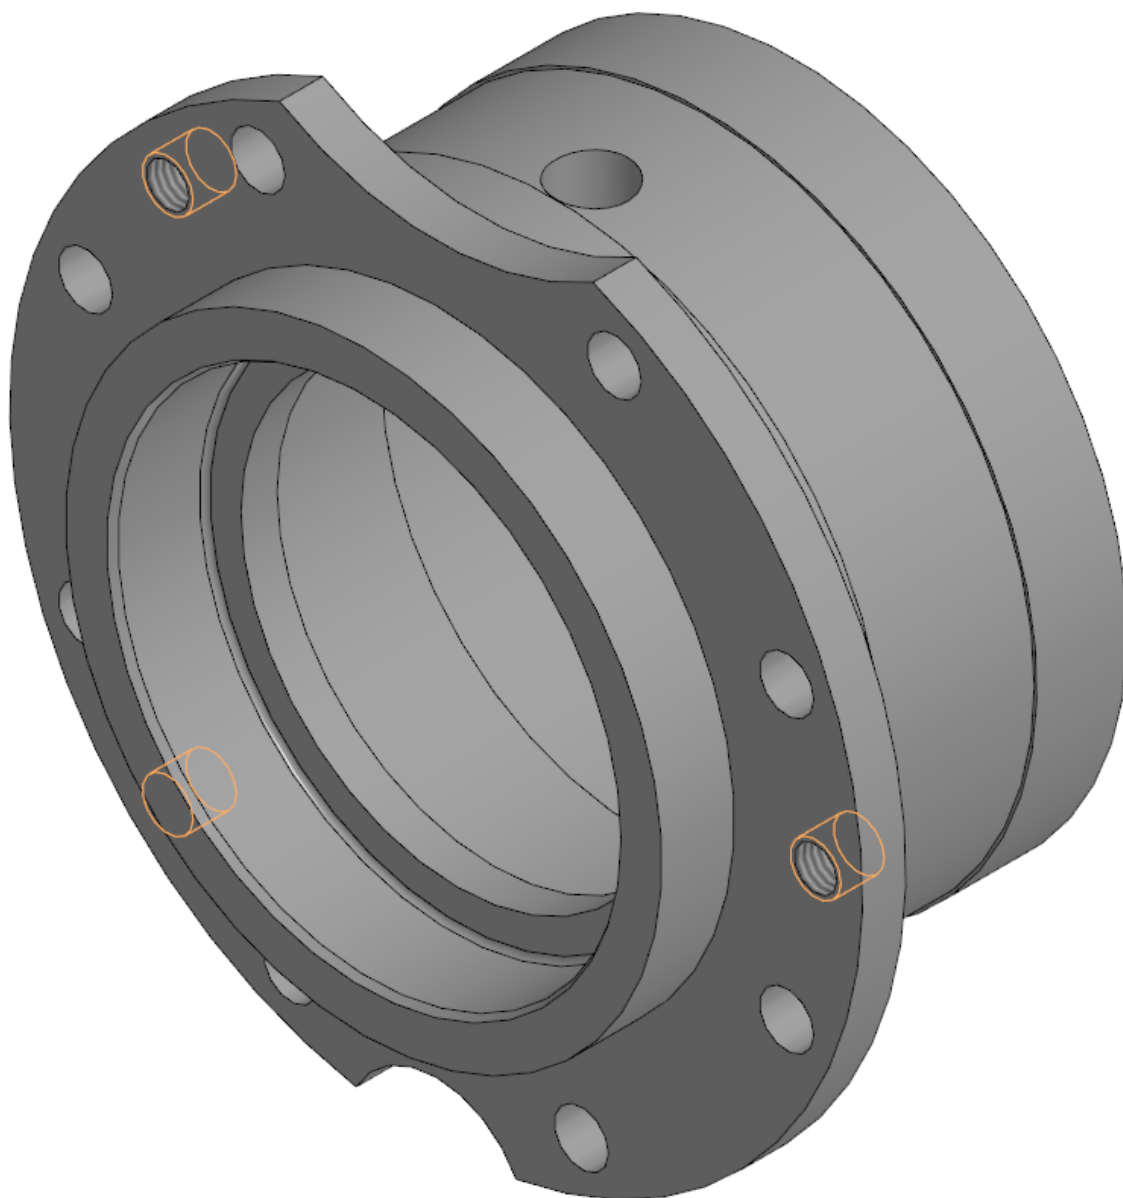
3D-модель детали «Стакан подшипниковый»
